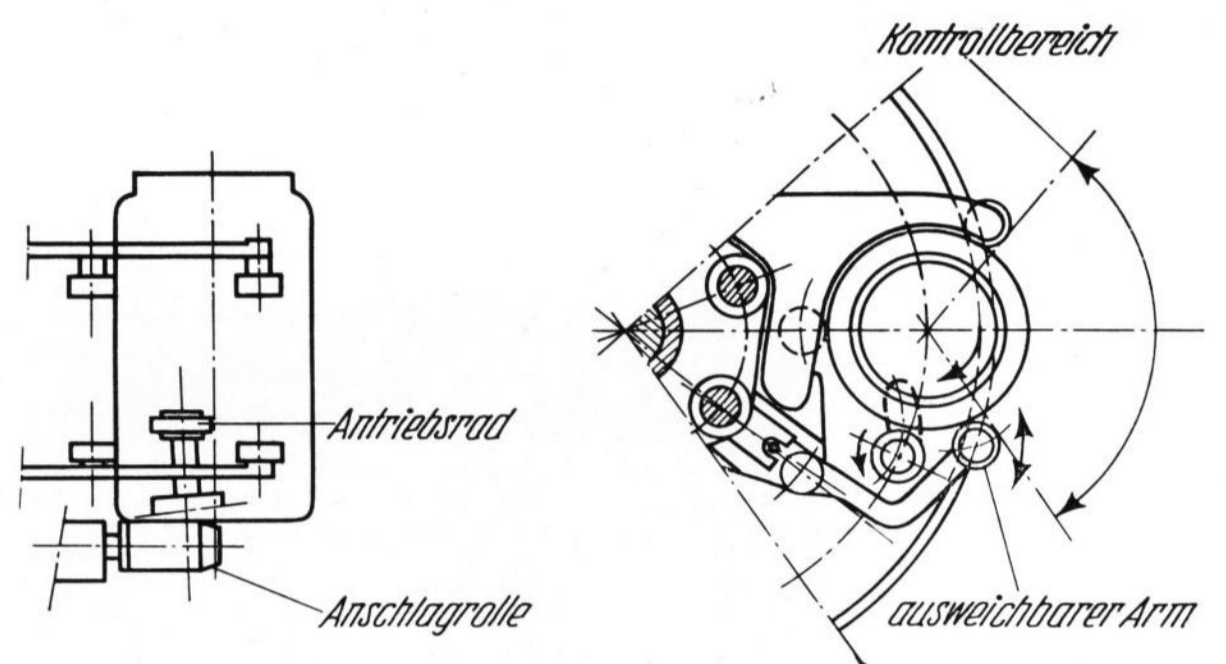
Fassung und Antrieb der Gläser in der Prüfmachine.
